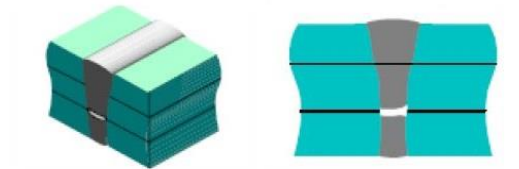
Schweißfehler „falscher Freund“ [6]
